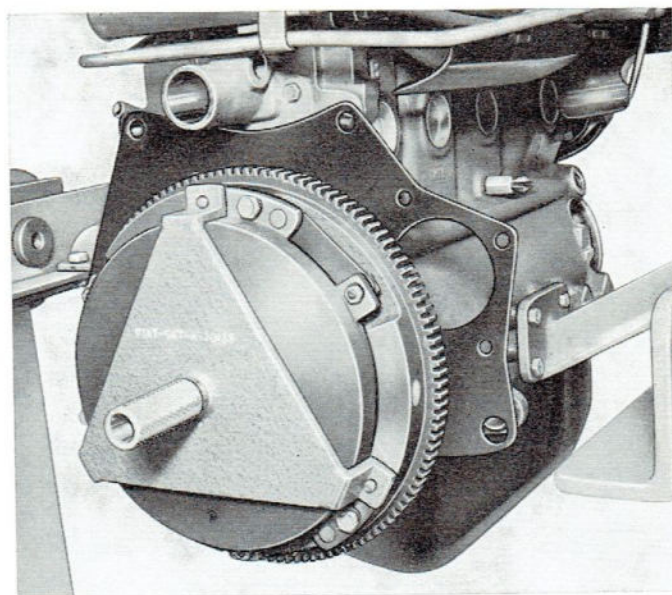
Zentrieren der Mitnehmerscheibe mit dem Werkzeug A. 70135.
